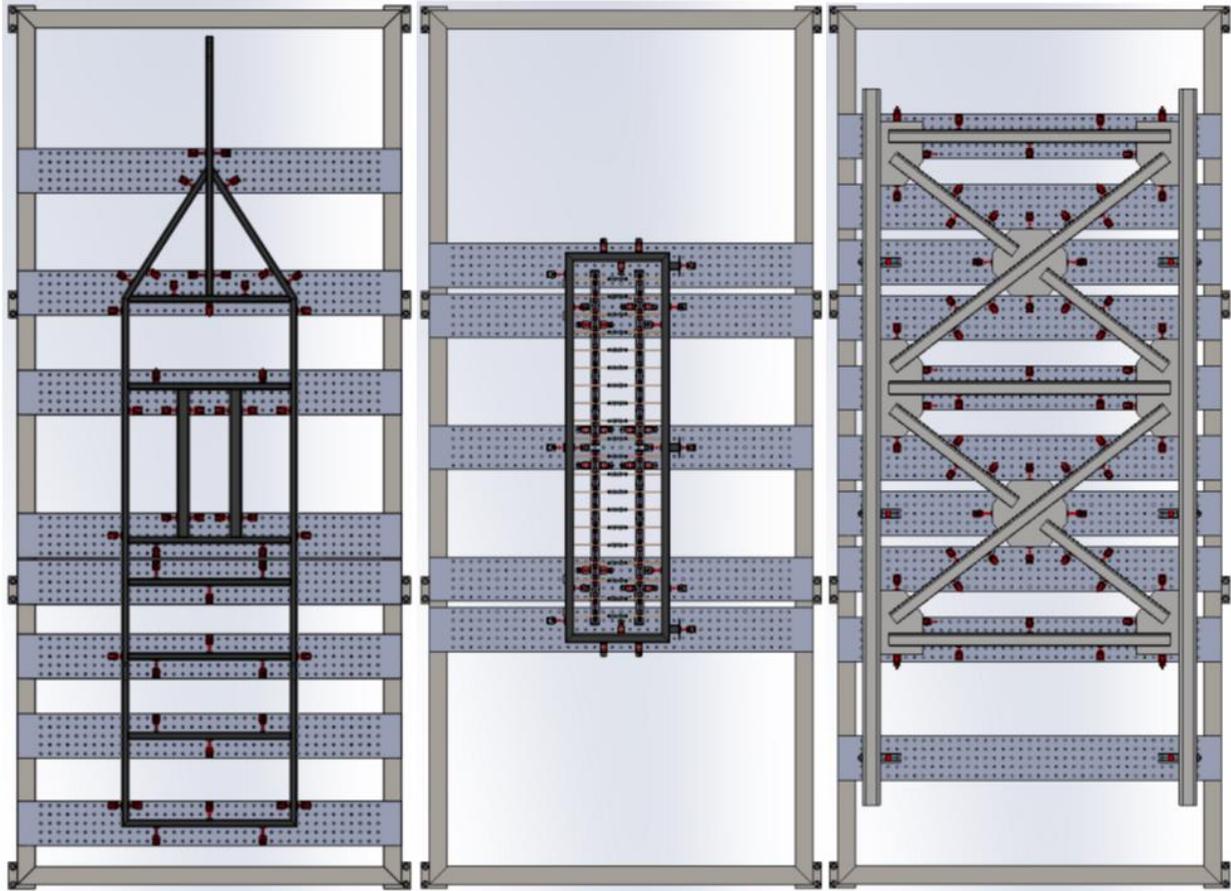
de izquierda a derecha, chasis de remolque, barandal, soporte estructural
